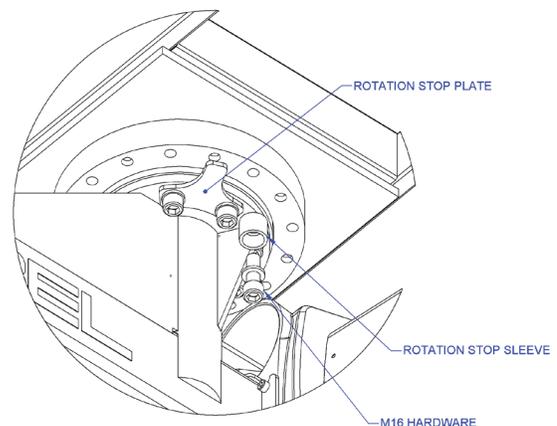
D. Installazione del blocco antirotazione del braccio con guida inferiore.
